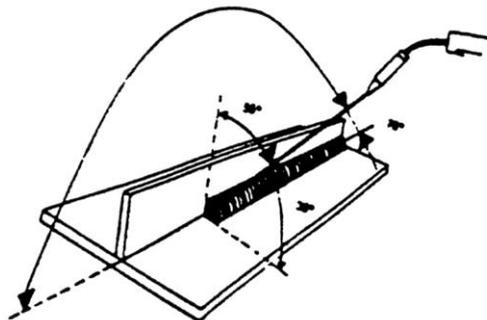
Lage des Brenners zur Schweißnaht
